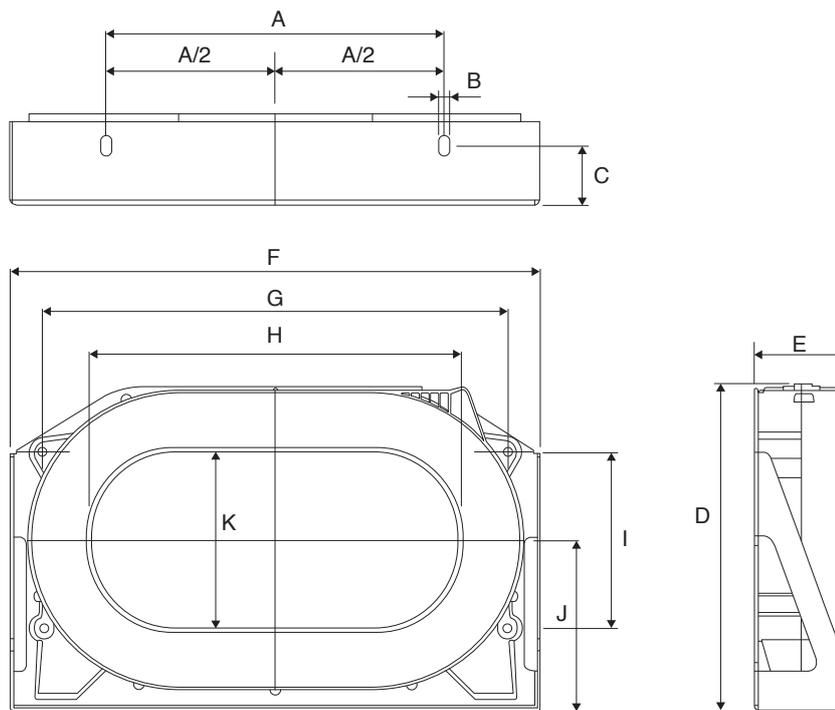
Dimensiones WGC 220x105, WGC 350x150 y WGC 500x200 (en mm).
